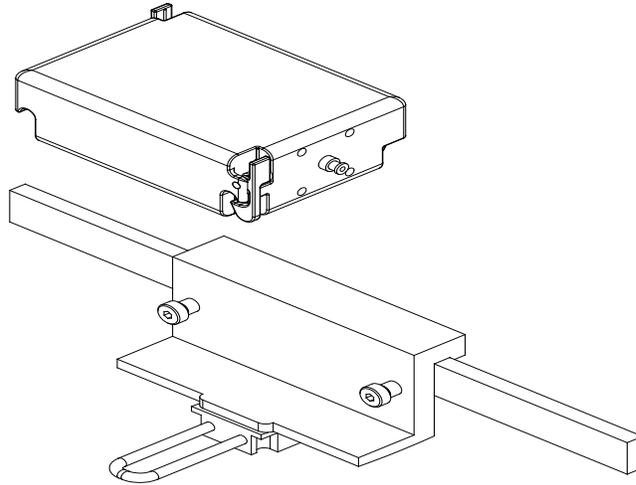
Installazione dei componenti di montaggio del gruppo del motore
